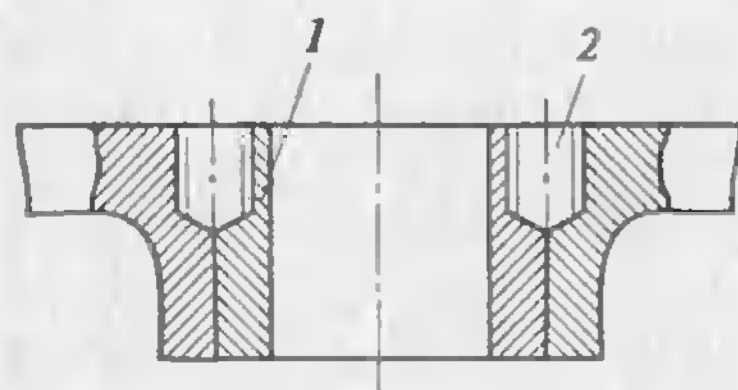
Ремонт посадочной поверхности подшипникового щита:
